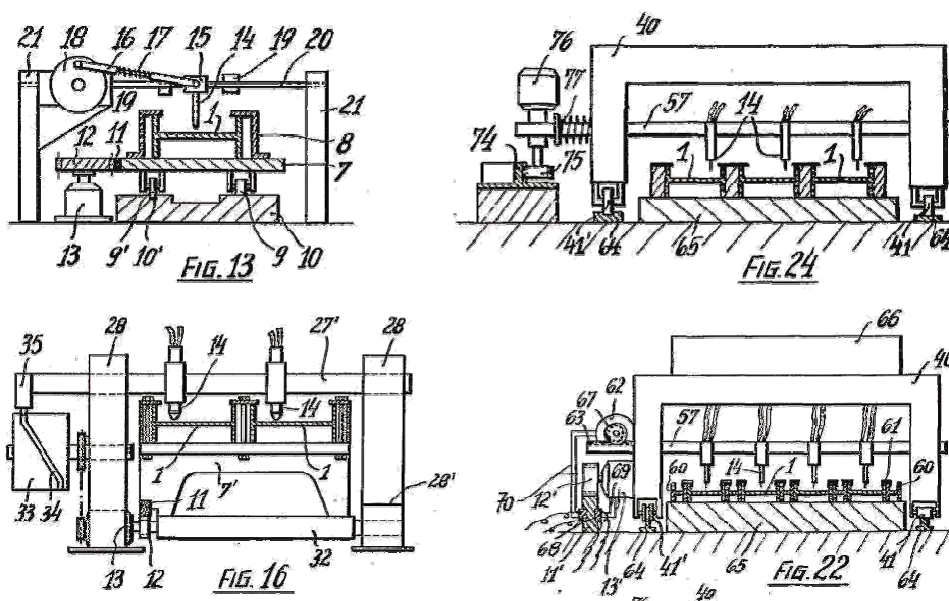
Esquemas das elevações dos aparatos para corte de vigas alveolares.
